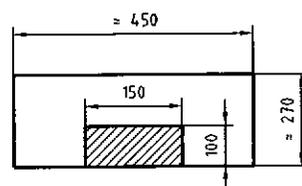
Exemple d'emplacement de la plate-forme de répartition de charge
